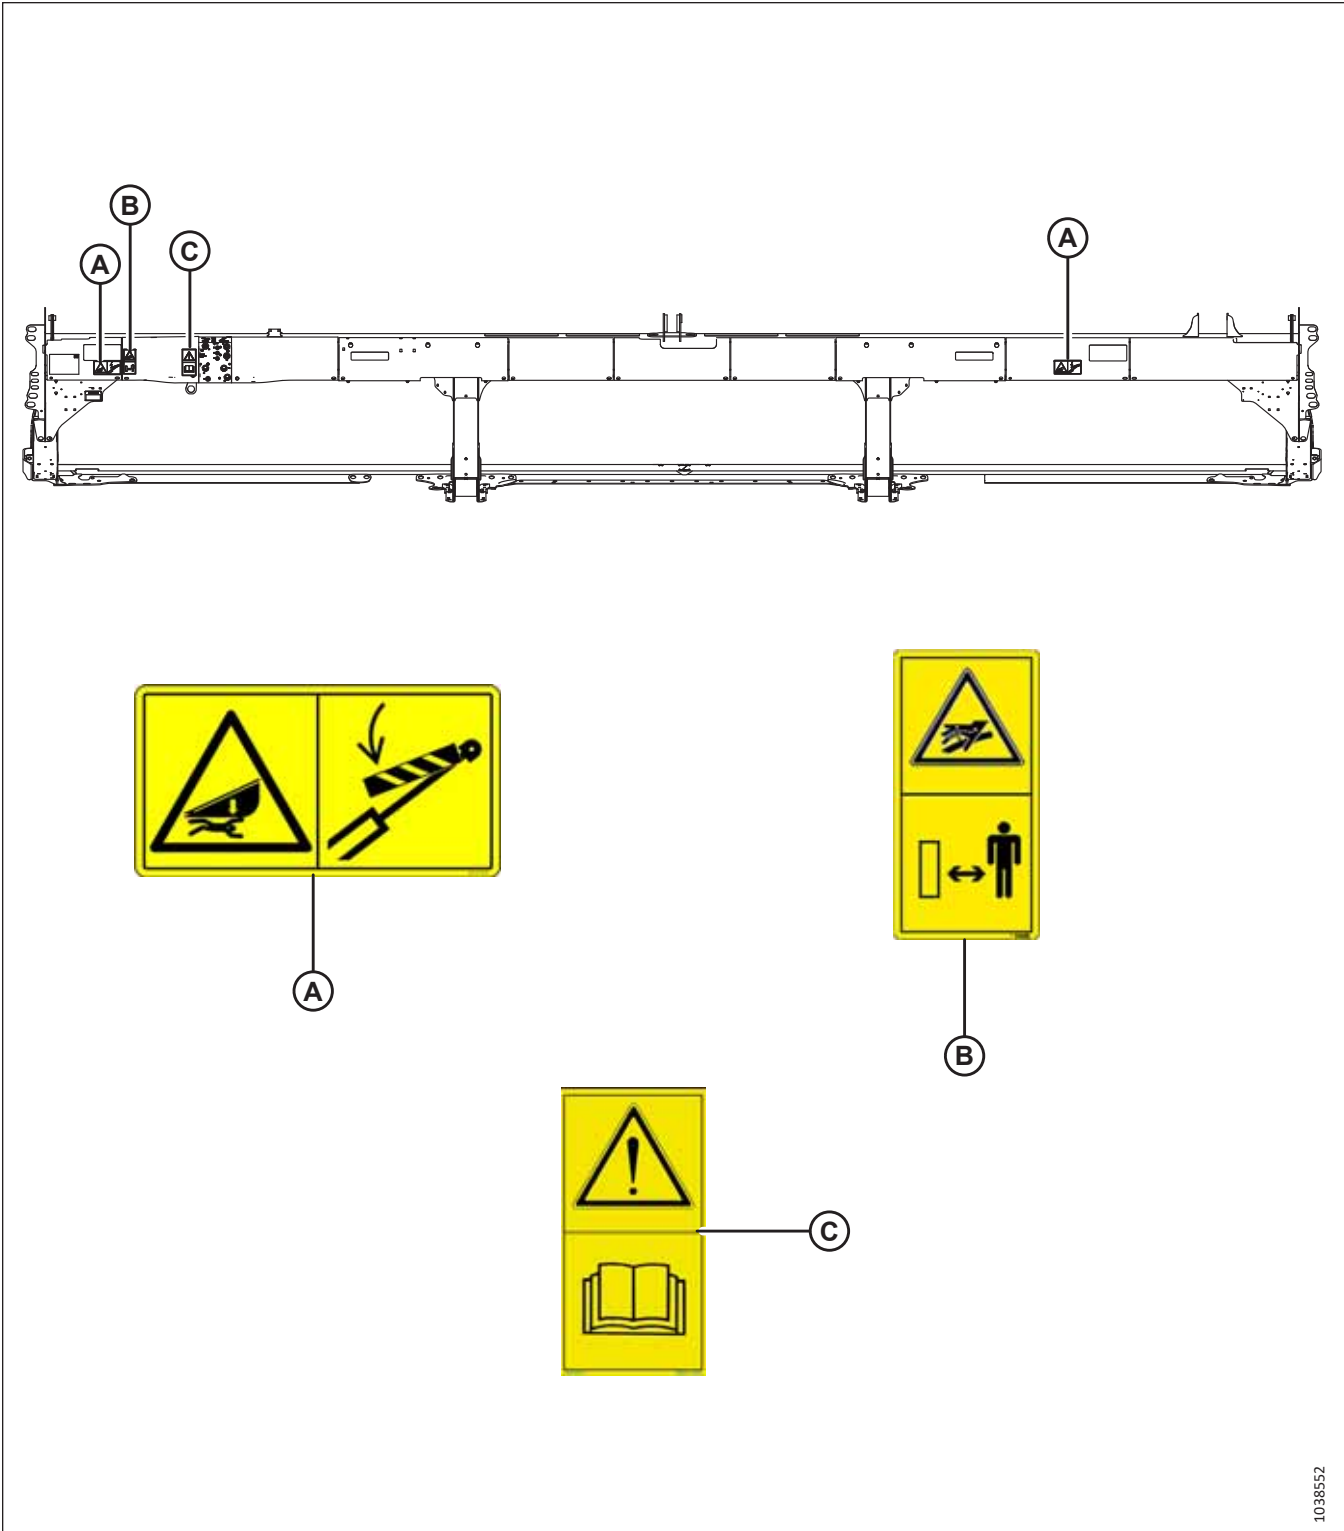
Tube arrière – Plateforme de coupe à tapis D225
